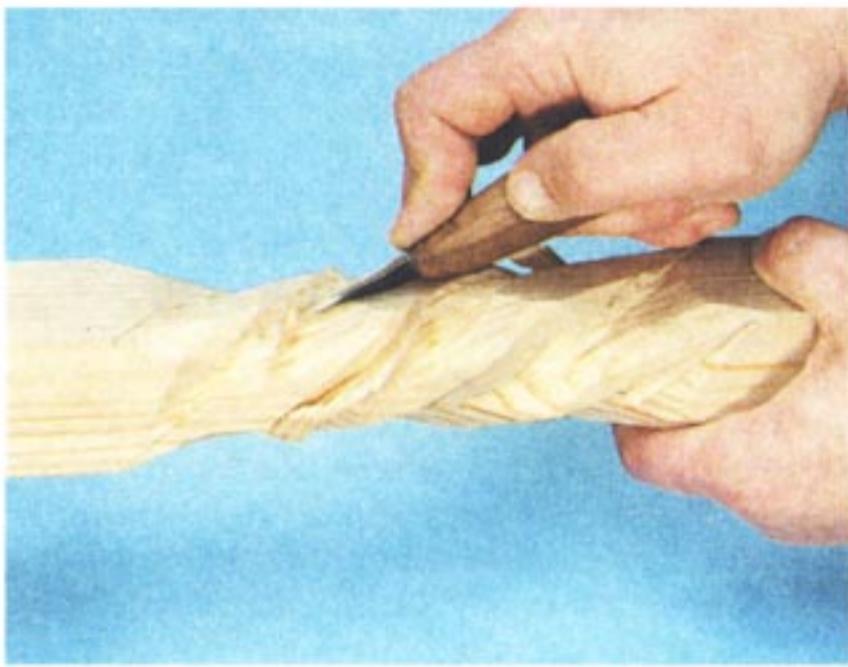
Грубый черновой сквозной проход по линии захода после разворота заготовки
